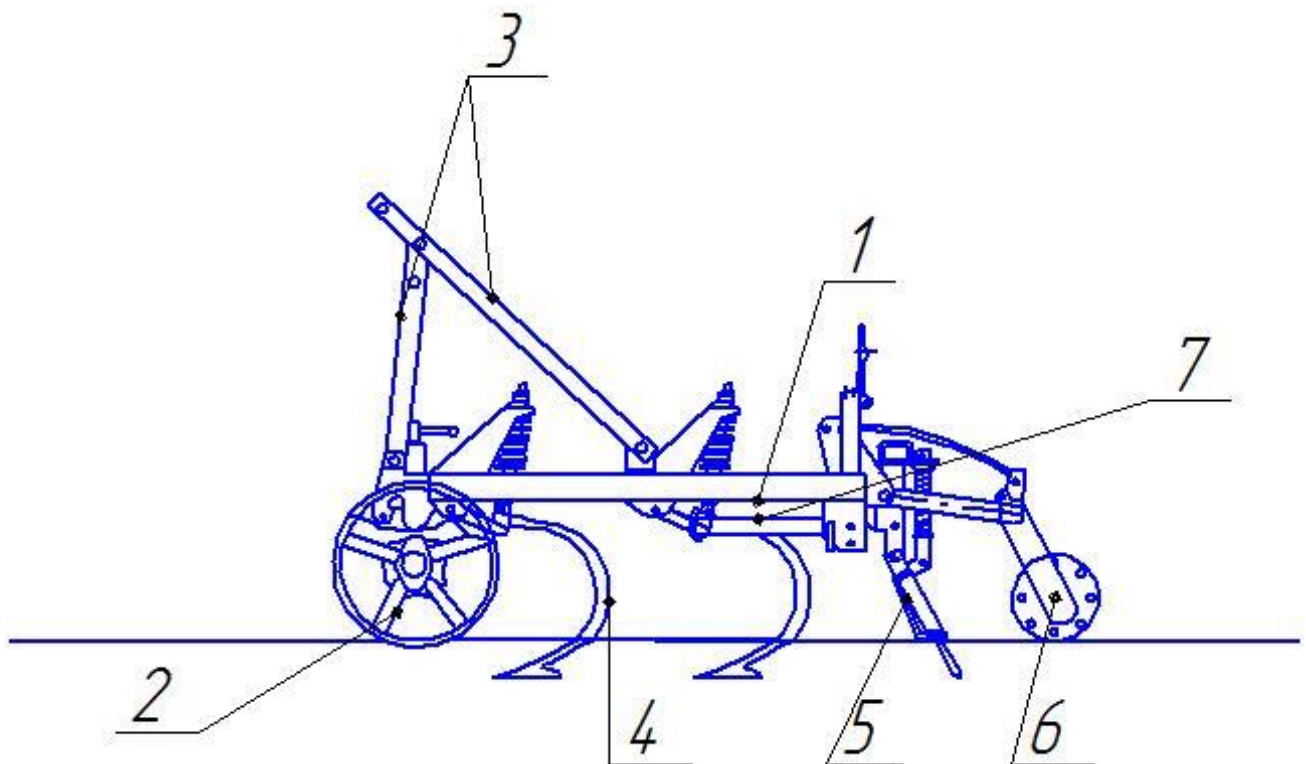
Культиватор комбінований КНК - 4Т: 1 – рама; 2 – опорне колесо; 3 – навісний пристрій; 4 – механізм навішування; 5 – вирівнювач ґрунту; 6 – прикочувальний пристрій; 7 – стійка.
